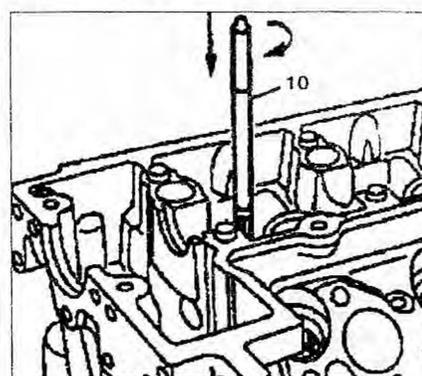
Установите фрезу-развертку и разверните диаметр в направлениях, указанных стрелками.
